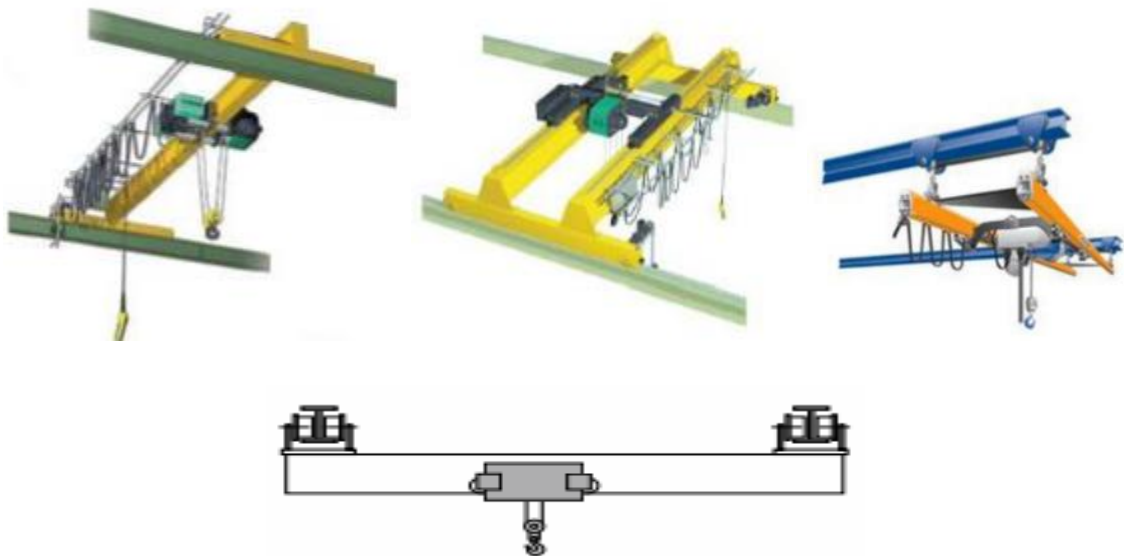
mono poutre suspendu et bipoutre suspendu [7].
